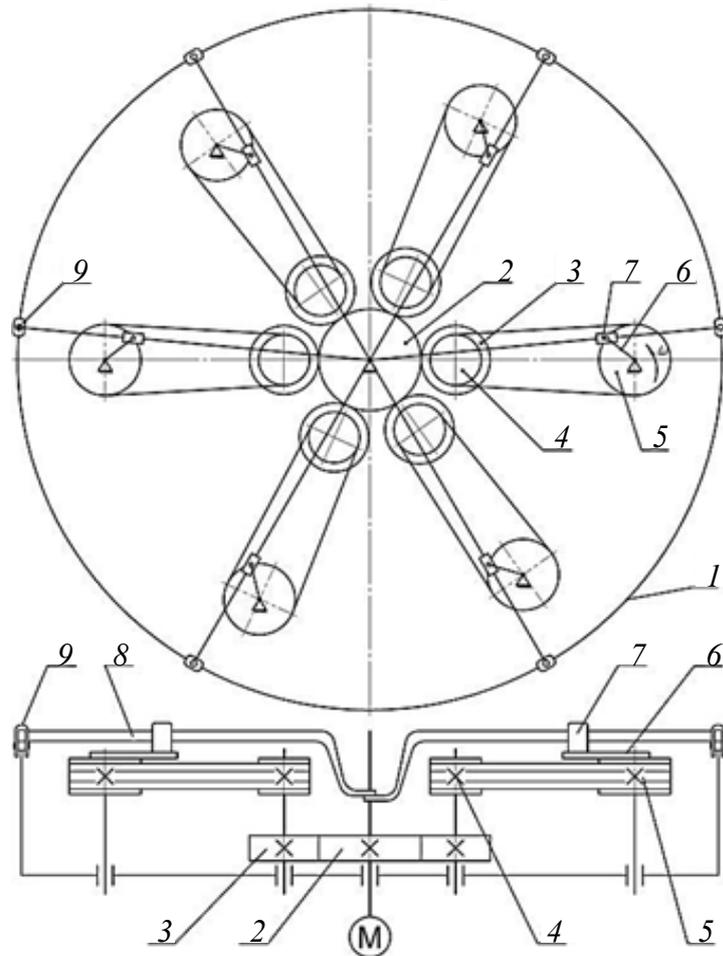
Плоский механизм основания с центральным вращательным приводом: вид сверху и вид слева
